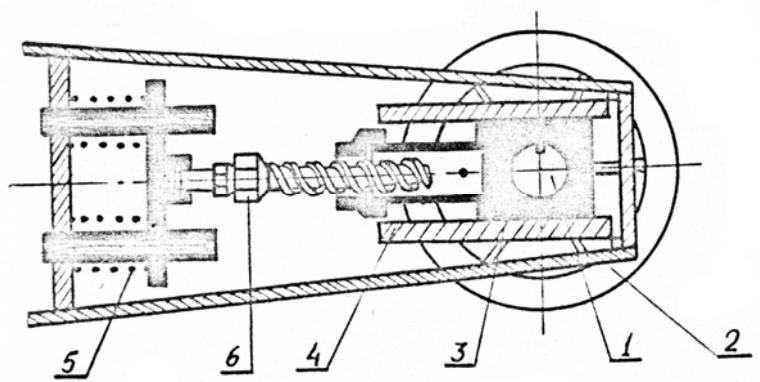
Установка натяжного барабана рабочего органа цепного многоковшового экскаватора.
